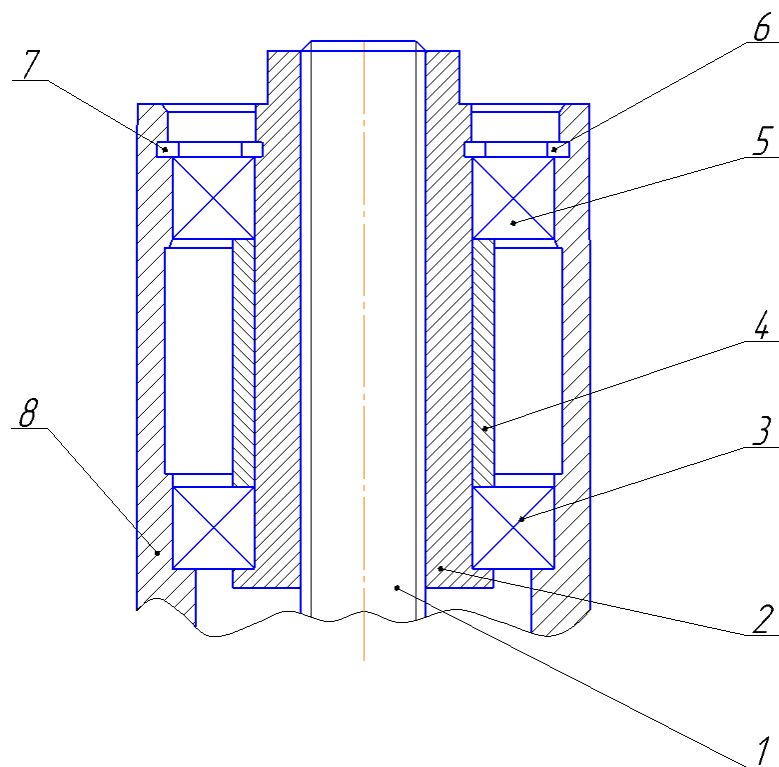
Підшипниковий вузол механізму регулювання висоти ротаційної закупорювальної машини
